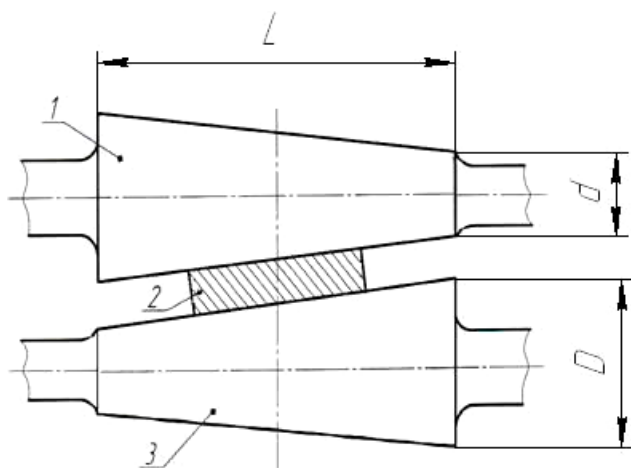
Схема прокатки в валках с обратной конусностью: 1 – верхний полуконусный валок; 2 – заготовка; 3 – нижний полуконусный валок
